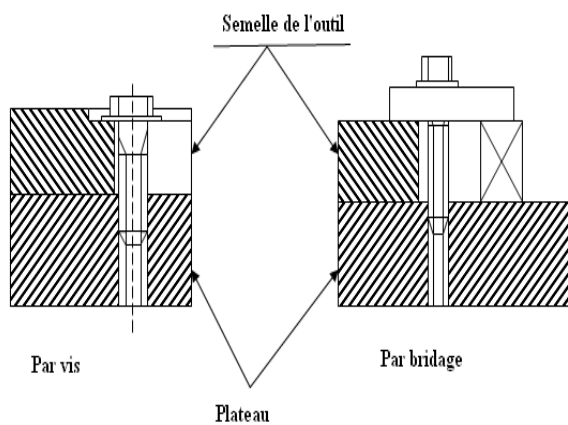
Système de fixation des semelles sur un plateau de presse.
